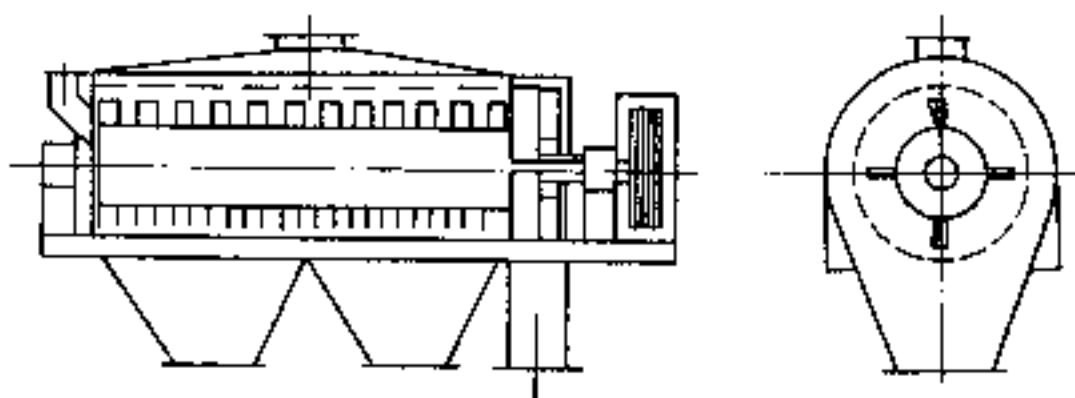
Схема конструкции классификатора (грохота) барабанного типа
